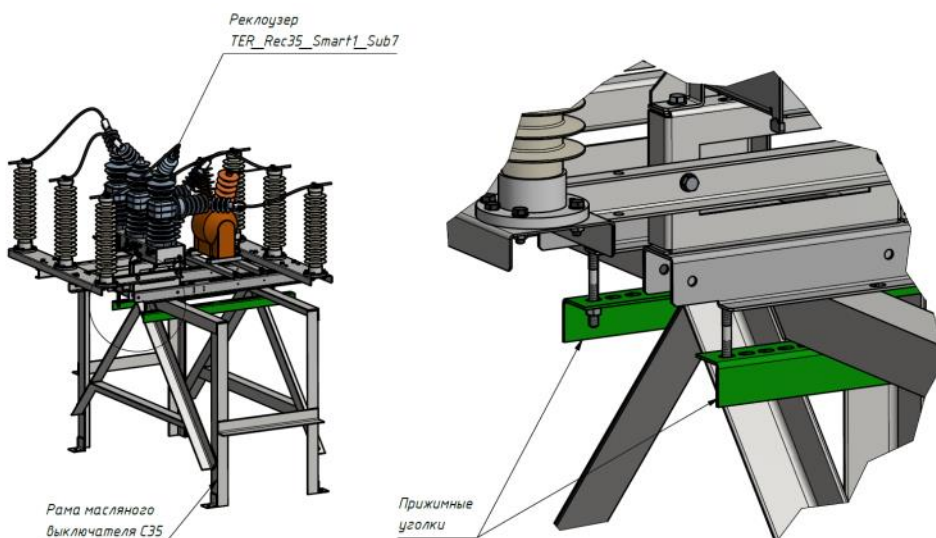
Крепление к раме масляного выключателя прижимными уголками
